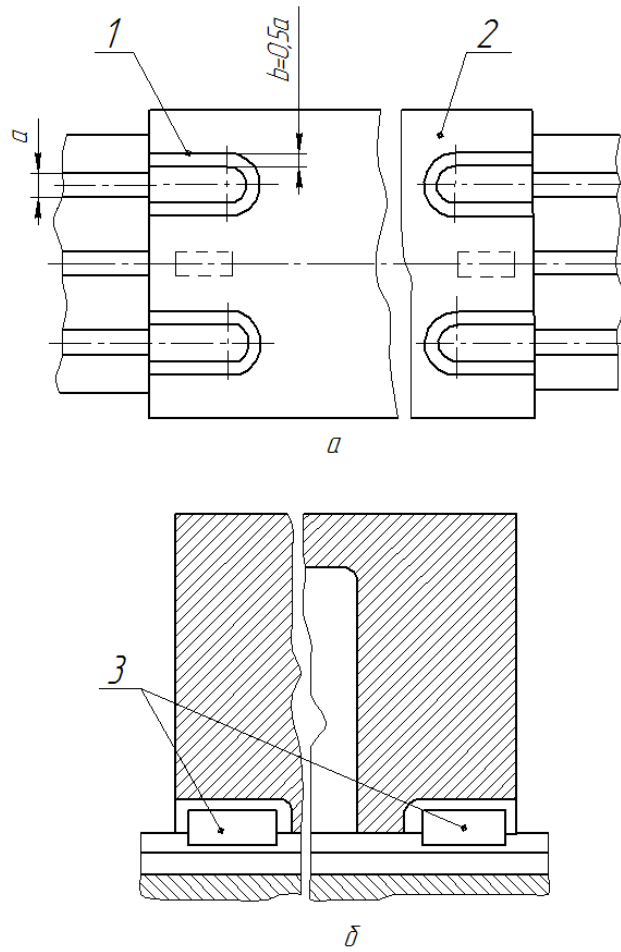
Схеми базування корпусу пристрою на столі верстата: *a* – кріплення корпусу за допомогою вушок 1 у пазах корпусу 2; *б* – попереднє орієнтування корпусу пристрою за допомогою шпонок 3
